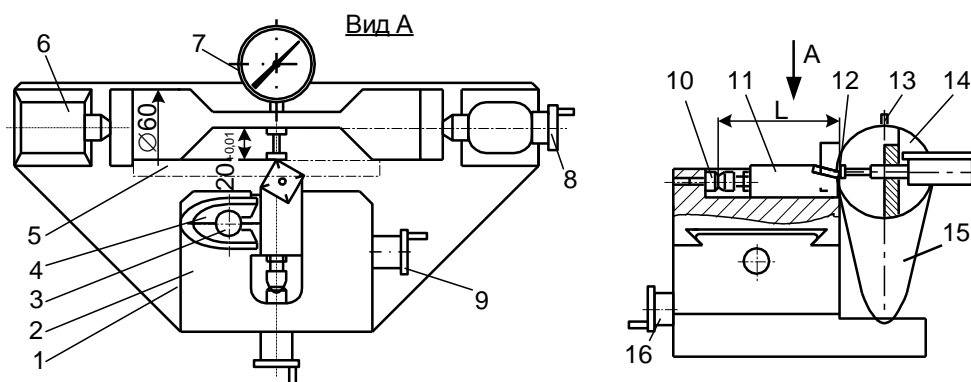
Схема индикаторного приспособления для исследования точности позиционирования резца: 1 - плита; 2 - резцедержавка; 3 - винт; 4 - клин; 5 - планка; 6 - центровая бабка; 7 - индикатор; 8 - рукоятка; 9 - рукоятка продольного перемещения; 10 - упор; 11 - резцовая вставка; 12 - вершина резца; 13 - рукоятка противовеса; 14 - оправка; 15 - противовес; 16 - рукоятка поперечного перемещения
